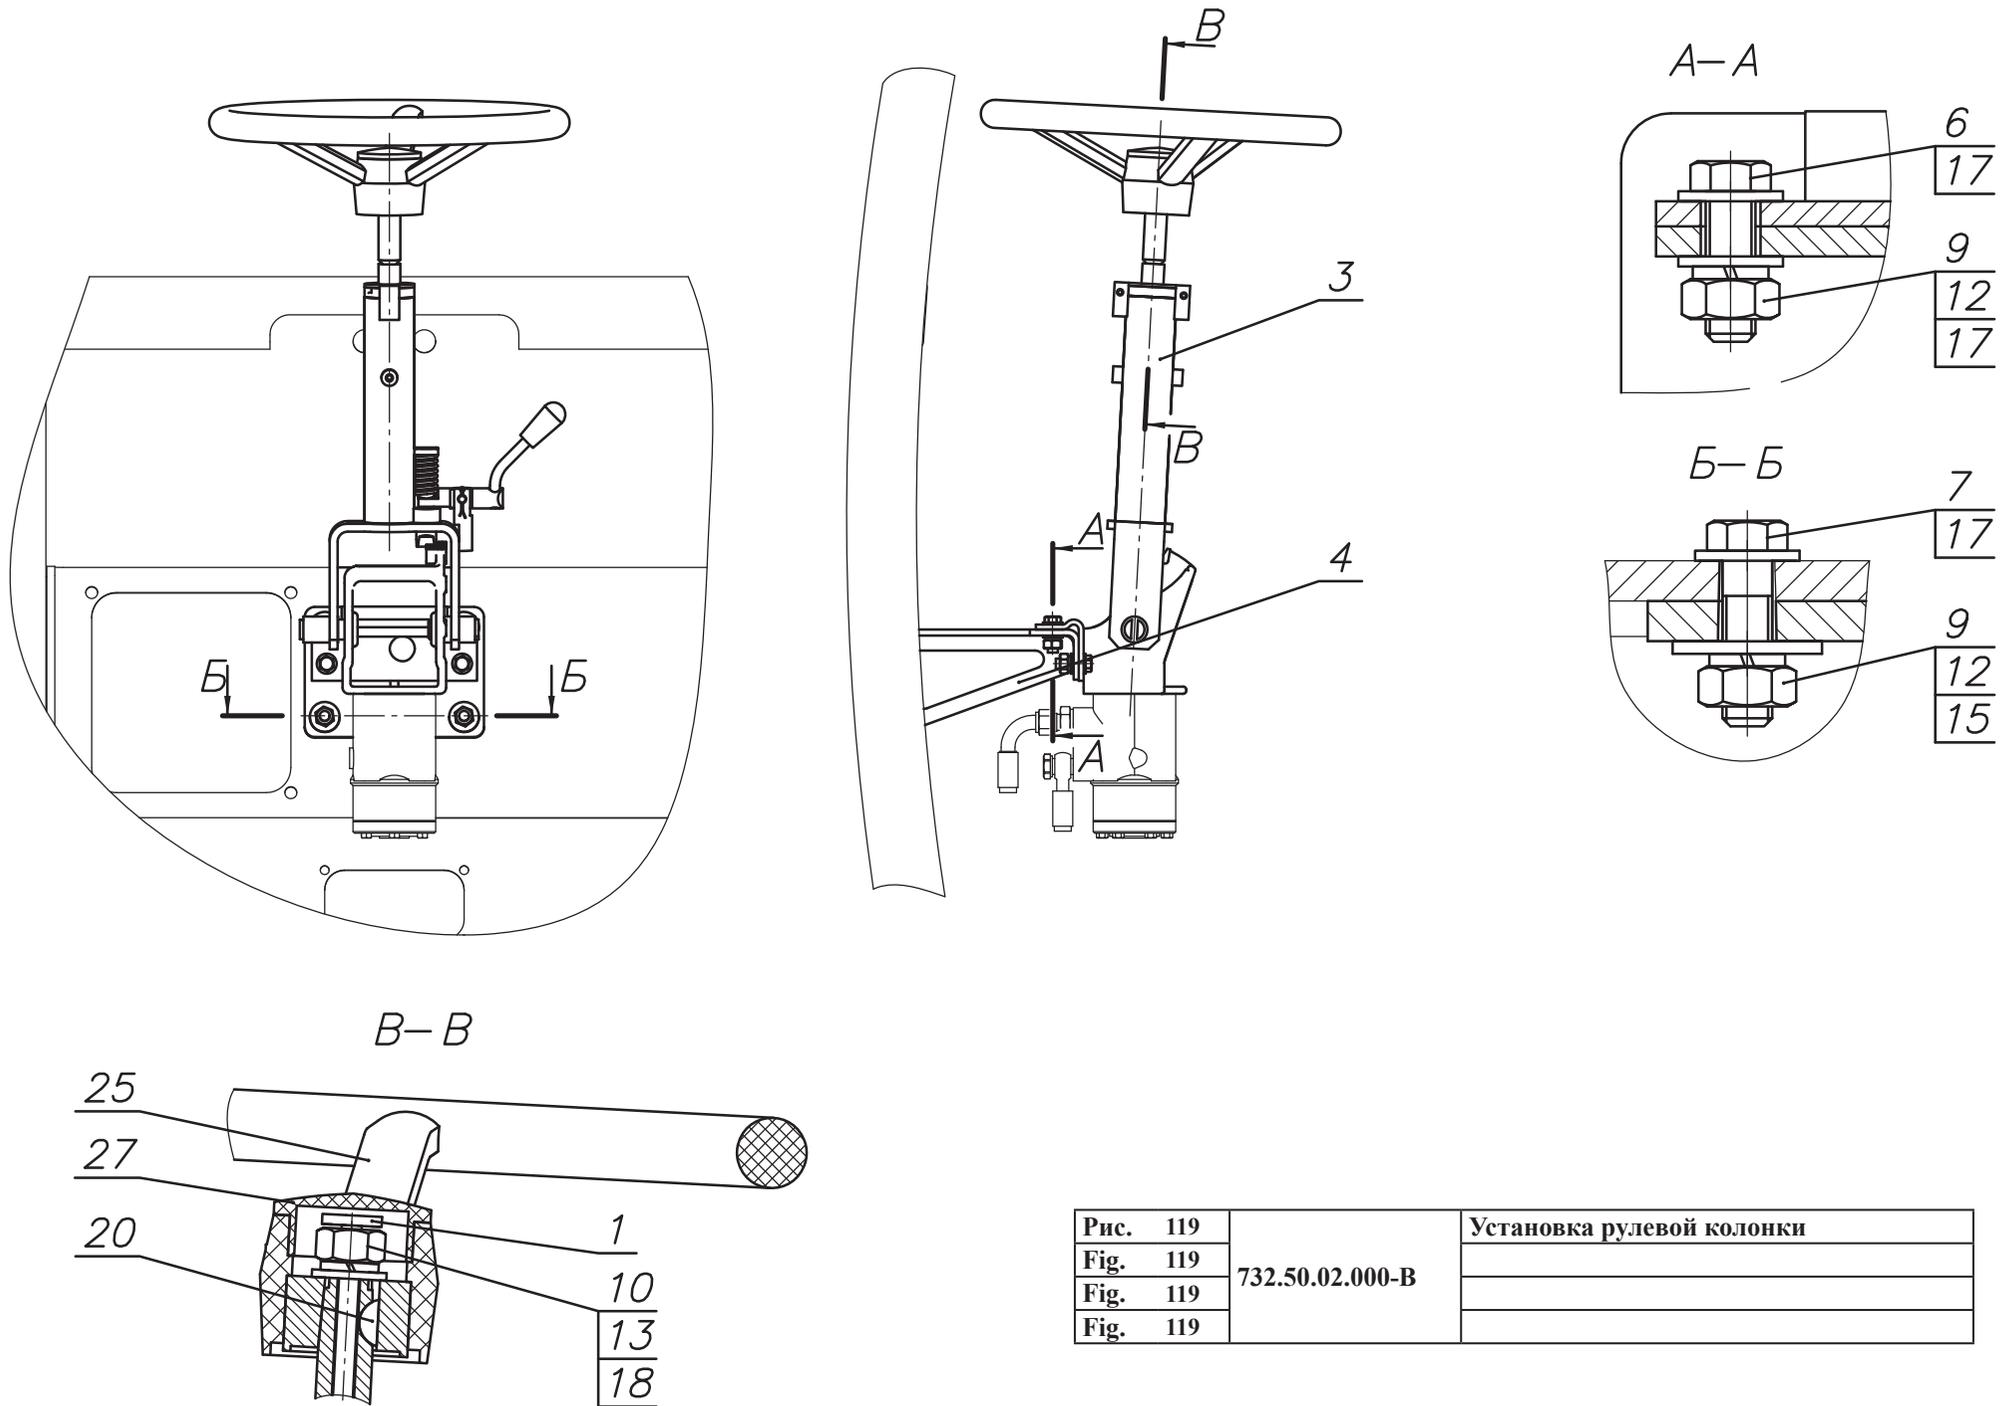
732.50.02.000-В	Установка рулевой колонки
